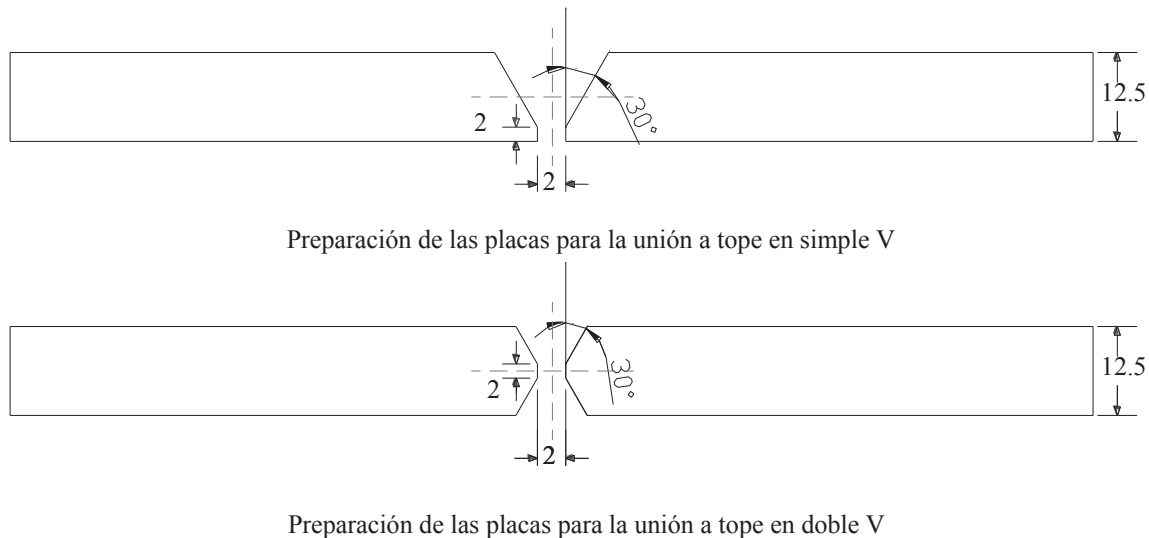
Tipos de juntas para las placas a soldar (a) simple “V” (b) doble “V” unidades en mm.
